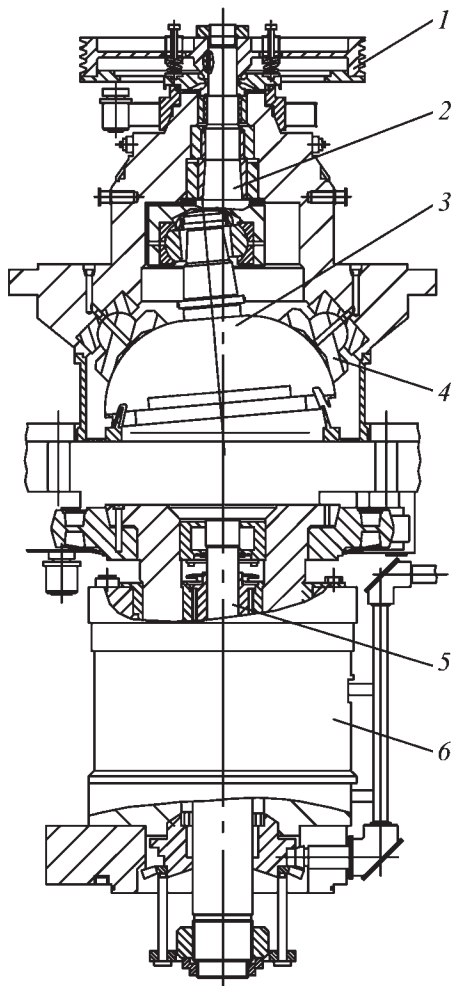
Схема конструкции пресса ВНИИТмаша:
